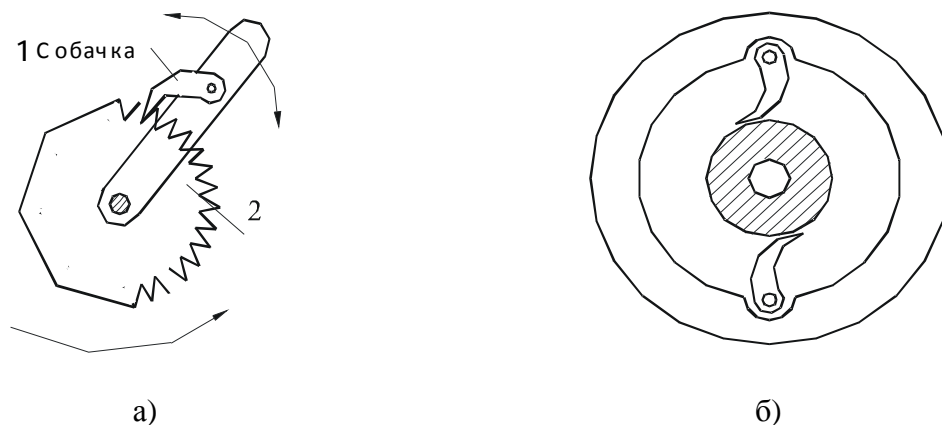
Храпові механізми: а – зубчастий механізм; б – фрикційний; 1 – собачка; 2 –храпове колесо
